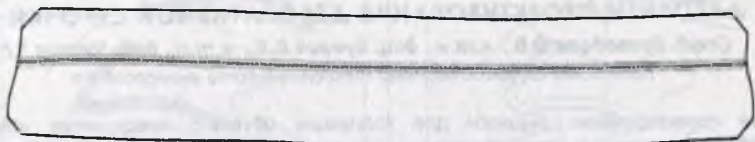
Деталь заготовки верха обуви с декоративной строчкой «симметричный гладьевого валик»
